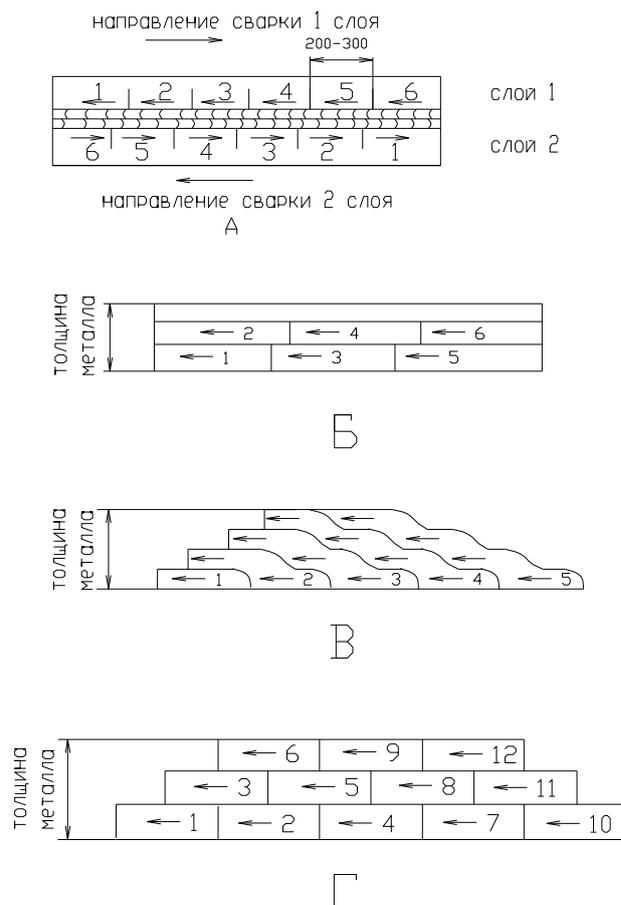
Схемы сварки обратноступенчатым способом (а), способом «двойного слоя» (б), горкой (в) и каскадом (г)
